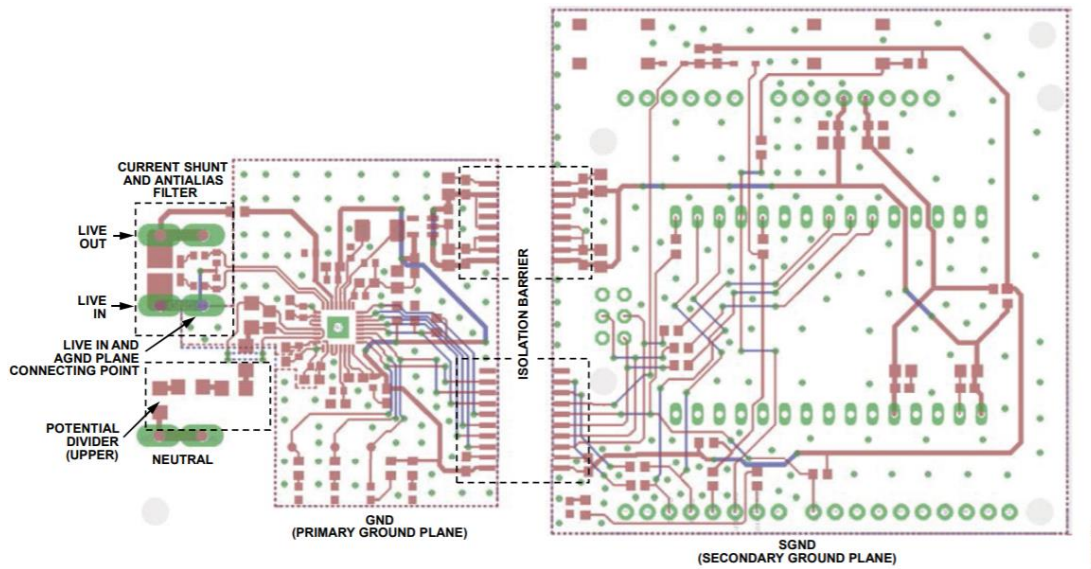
[EV-ADE9153ASHIELDZ](#) PCB。
